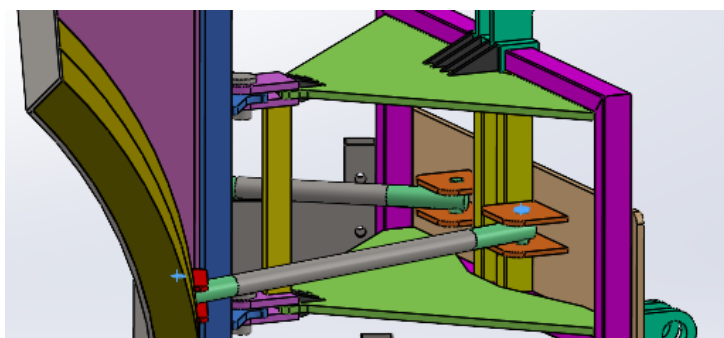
Imagen que muestra la posición central de las uniones a la estructura de conexión.
